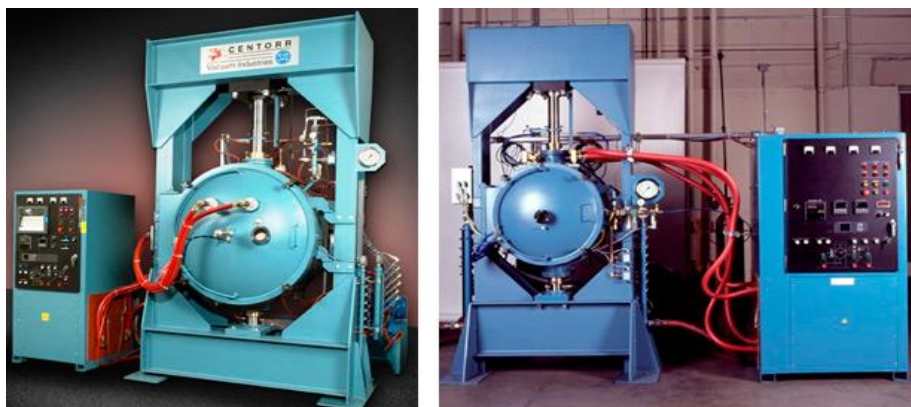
Прессы горячего прессования Centorr/VacuumIndustries для композиционных материалов на основе керамической или металлокерамической матрицы
